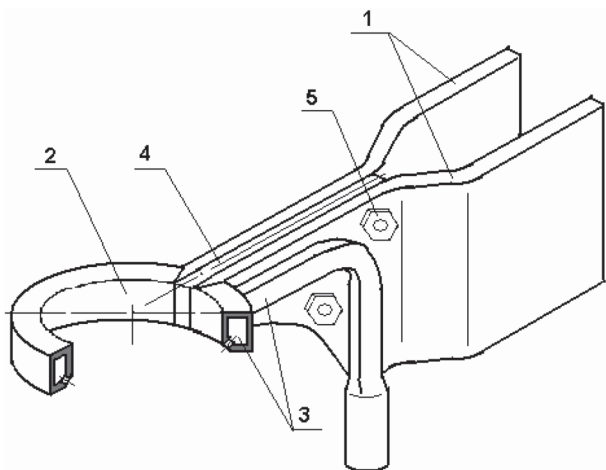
Индуктор для непрерывно-последовательной закалки деталей типа вал: 1 – шина; 2 – индукционный виток; 3 – система закалки – охлаждения; 4 – изоляция; 5 – крепежные изделия
